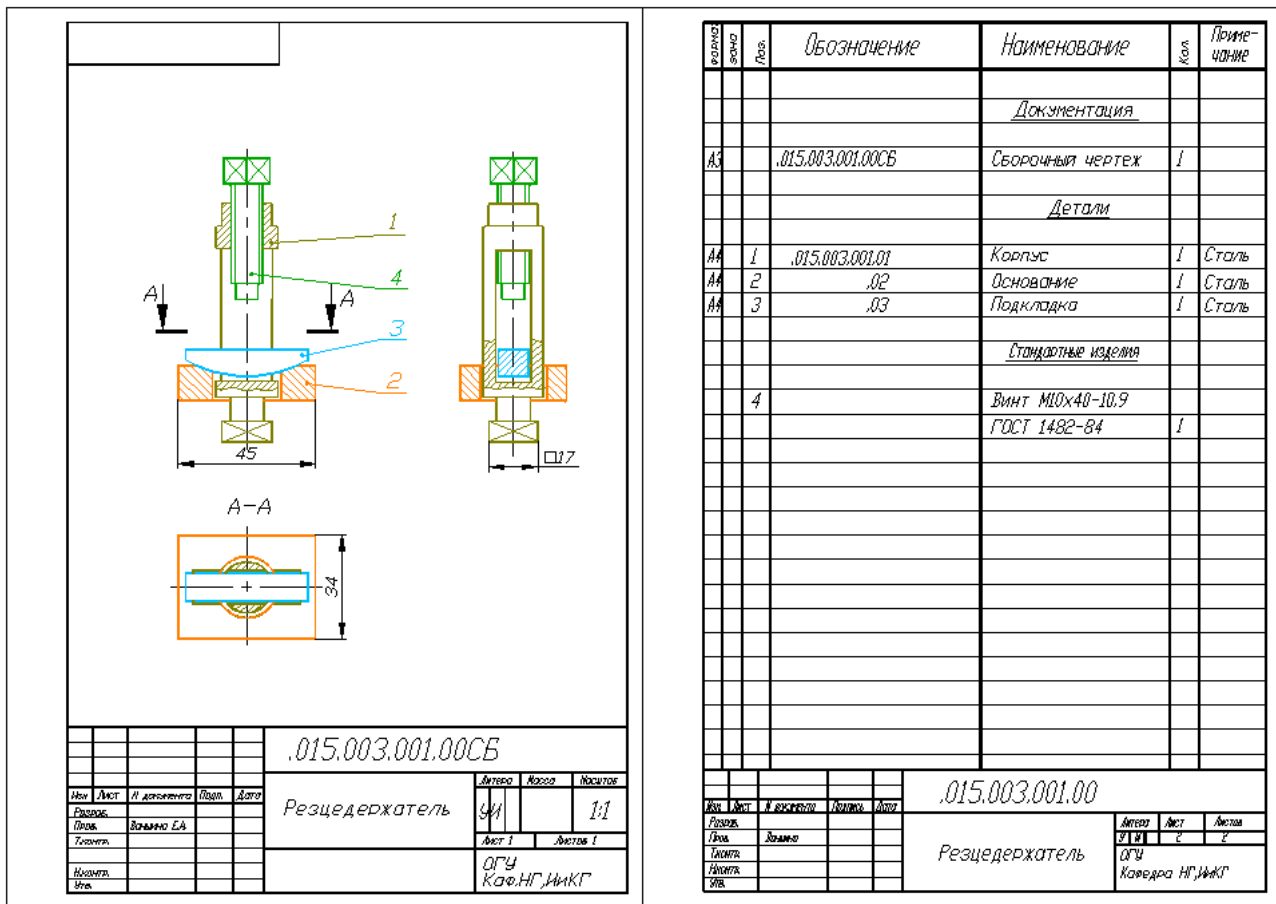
Сборочный чертеж «Резцедержатель».
